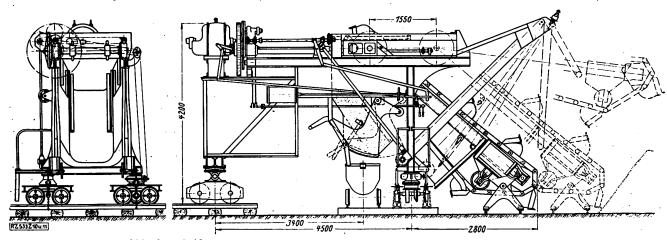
und 10 Eimerbagger der Maschinenfabrik Buckau
